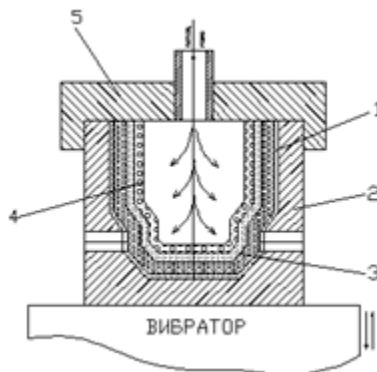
Контейнер для изготовления . 1-спеченная пористая заготовка;
